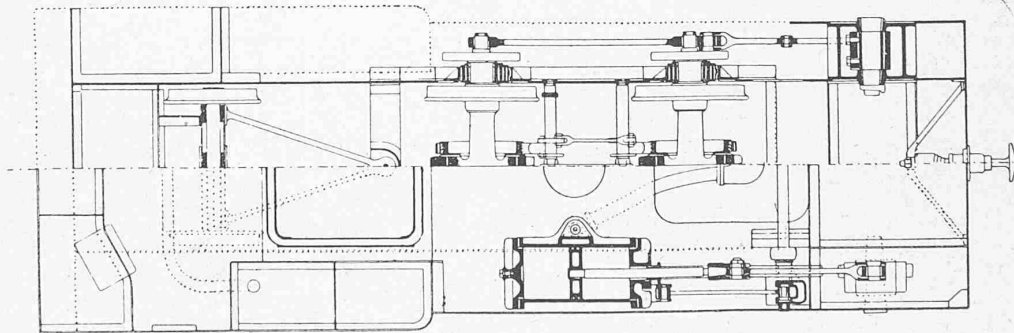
Grundriss und Horizontalschnitt.
